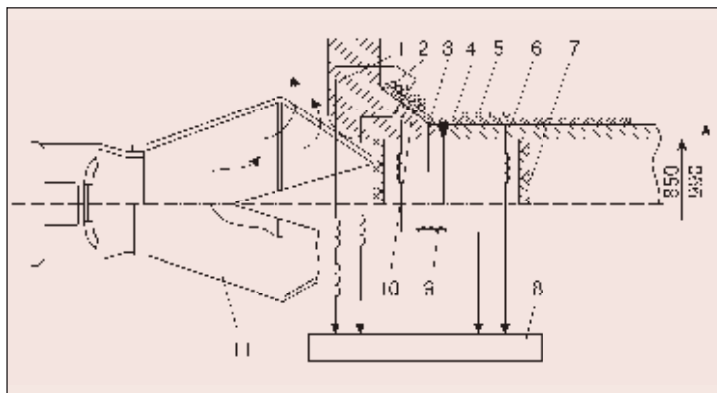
Схемы проведения термической обработки сварного соединения трубопровода I контура с патрубком корпуса реактора ВВЭР-1000: 1 — патрубок; 2 — индуктор, установленный на патрубке; 3 — ограничительные штыри; 4 — теплоизоляция зоны сварного шва; 5 — индуктор, установленный на трубе; 6 — теплоизоляция участка трубы; 7 — внутренние теплоизоляционные перегородки; 8 — шкаф управления установкой для термической обработки; 9 — регулирующие дроссели в цепи индукторов; 10 — теплоизоляция патрубка; 11 — осевой вентилятор с диффузором
